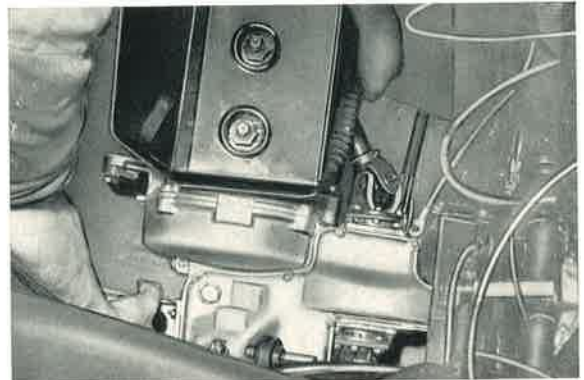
Der freie Motor wird zunächst links nach vorn oben angekippt, damit die lange Gelenkwelle aus ihrer Führung im Gelenk von selbst herausrutscht.
